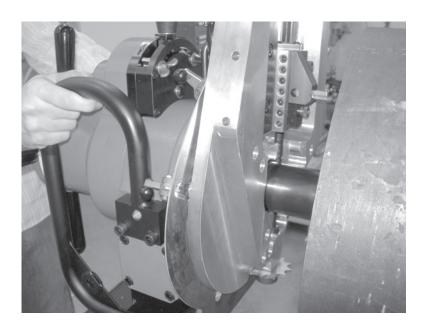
Толкайте станок вперед на оправку до сцепления резьбы оправки с гайкой механизма подачи.
